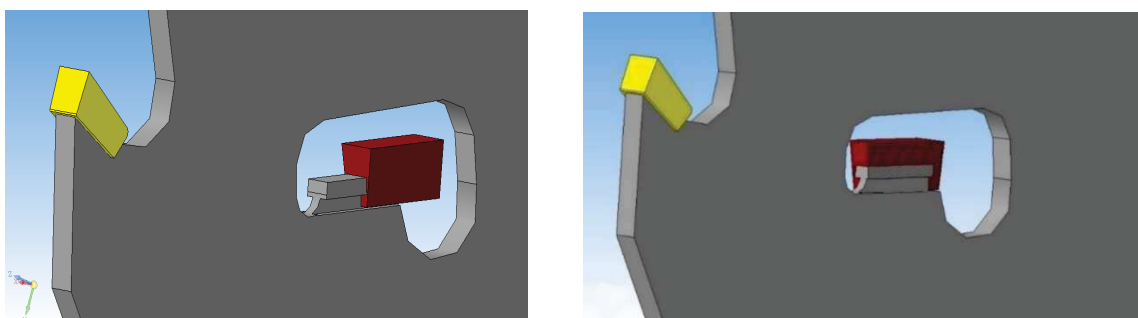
Схема крепления стабилизирующего ножа к полотну пилы
